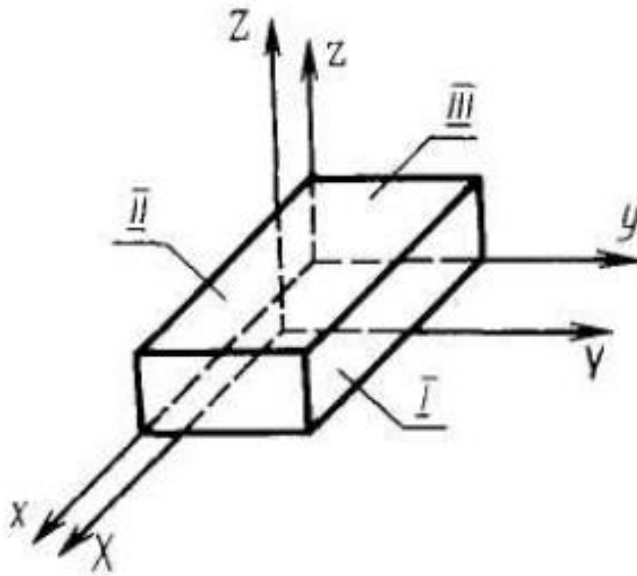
Комплект баз призматической заготовки: I, II, III – базы заготовки
